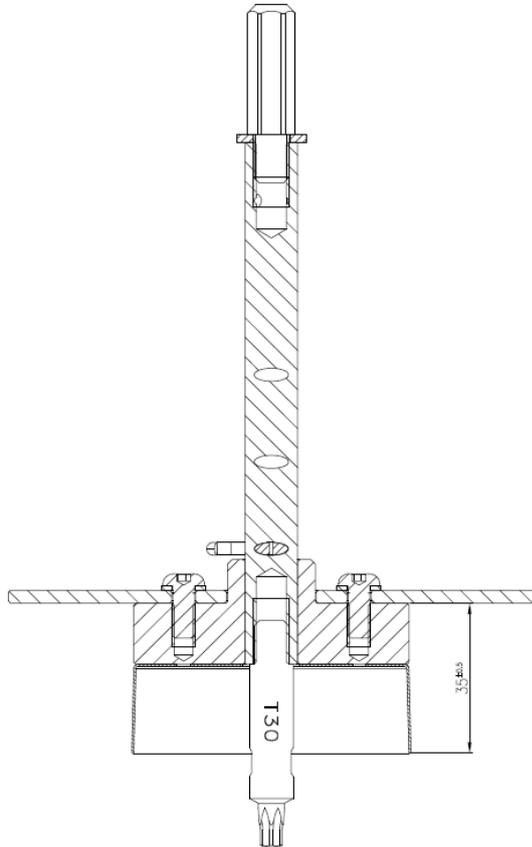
ejotherm STR U 2G Montagewerkzeug Typ "L"
